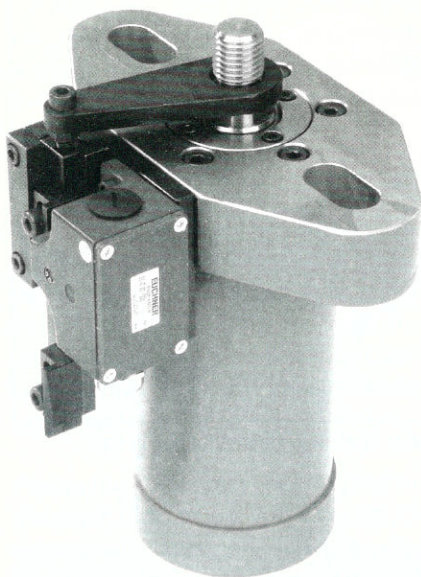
Kernzugzylinder mit einstellbaren Positionsschaltern.
